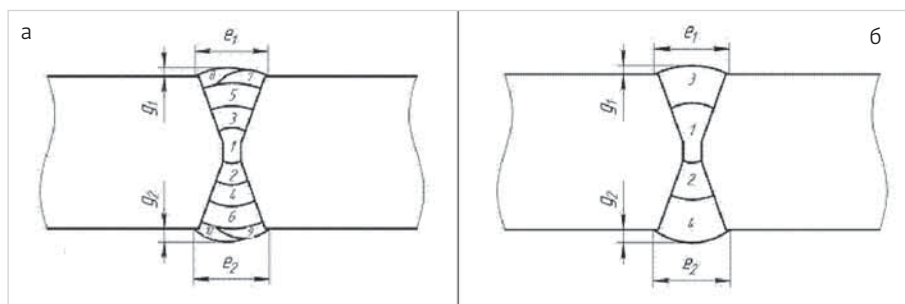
Схема раскладки валиков при механизированной сварке в среде защитного газа (а) и при автоматической сварке под флюсом (б)
